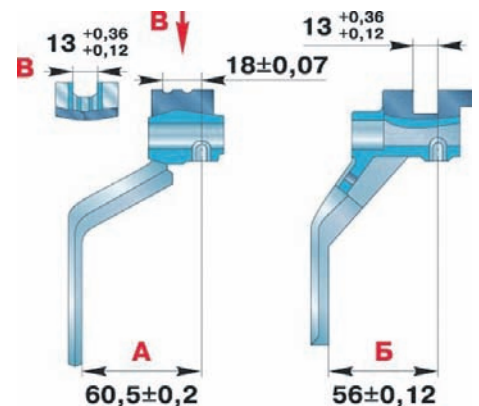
Контрольні розміри вилок перемикачів коробки передач, синхронізованої частково: А – вилка I, II передач; Б – вилка III, IV передач
